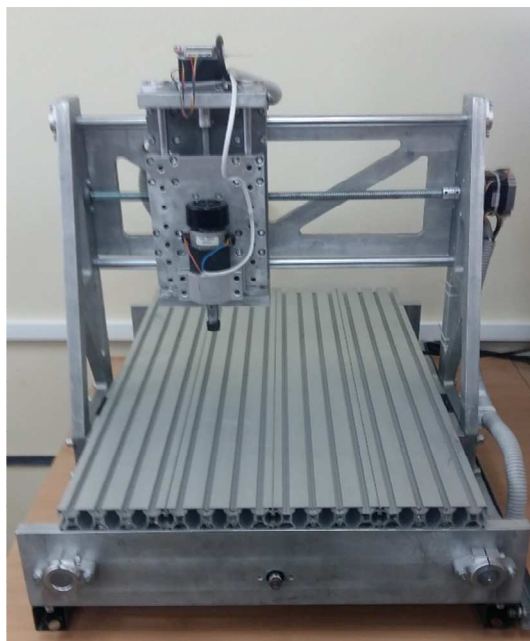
Трикоординатний фрезерний верстат з ЧПК моделі CN 2
